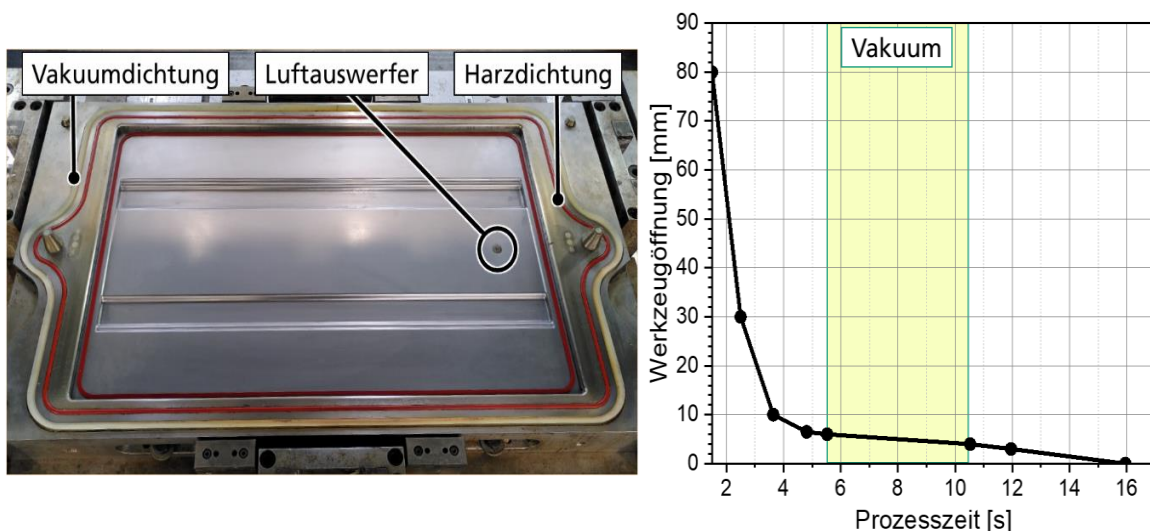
Werkzeugunterseite inklusive Harz- und Vakuumdichtung sowie der Luftauswerfer (links); Weggeregeltes Werkzeug-Schließprofil (rechts)
